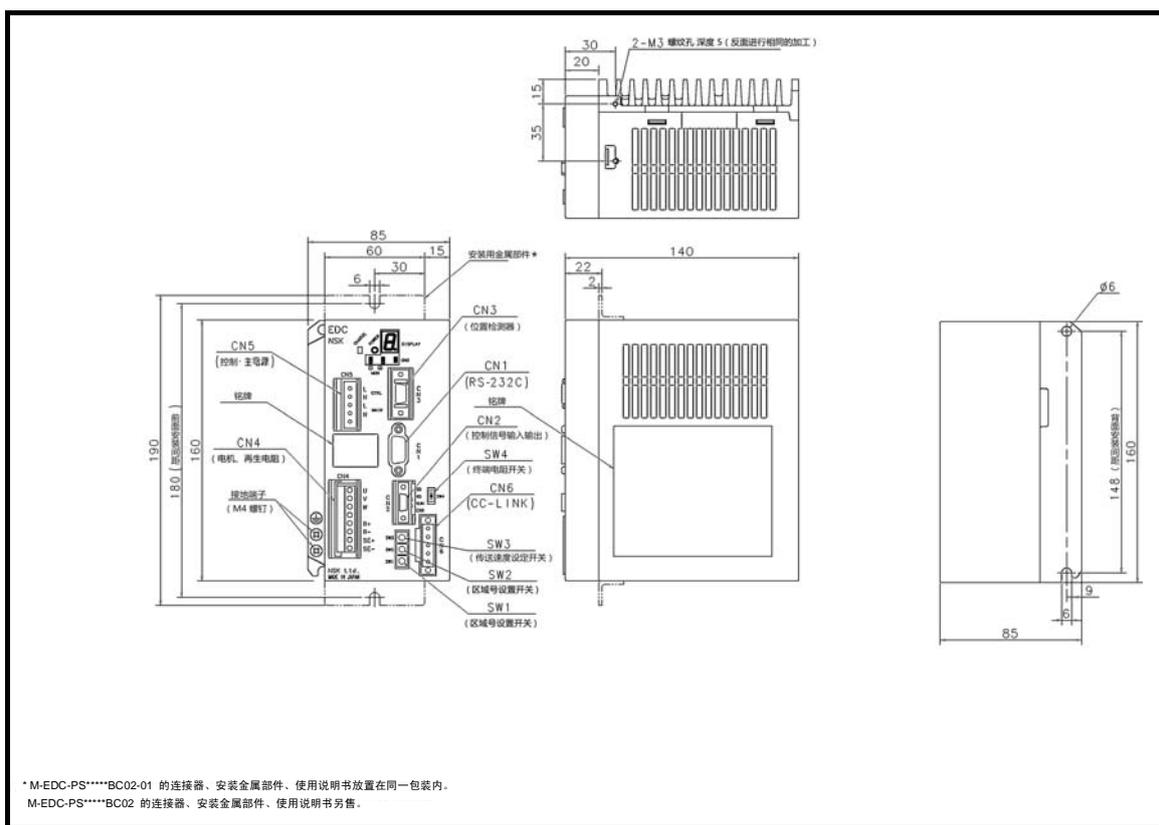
支持 CC-Link 的 EDC 型驱动器外形尺寸
